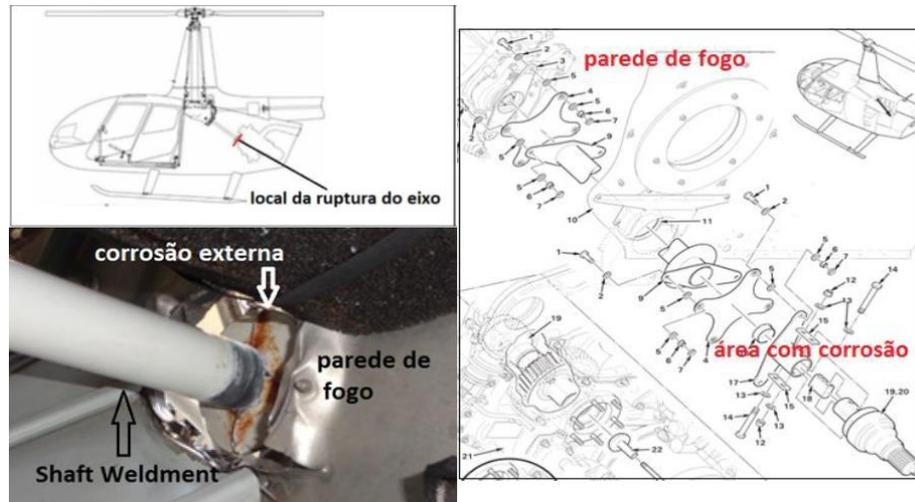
Local de quebra do eixo (esquerda superior); Imagem do componente quebrado (esquerda inferior); vista explodida do componente quebrado (direita) [17].
